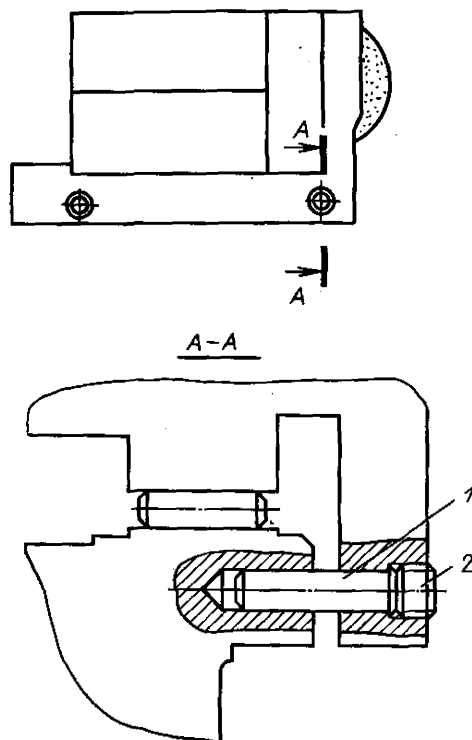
Схема закрепления шлифовальной бабки при транспортировании станка
